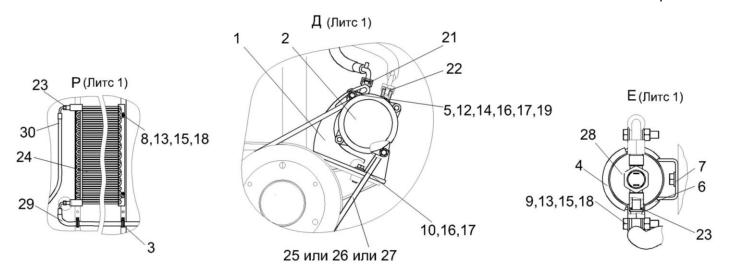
Установка компрессора КЗК-7-0113030-01 (лист 1)
